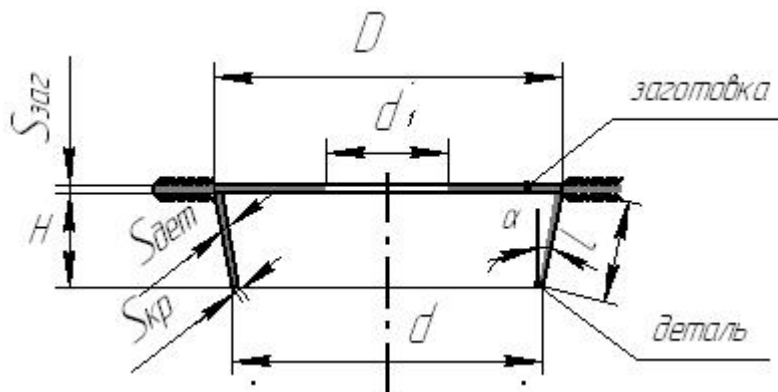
Схема процесса отбортовки из кольцевой заготовки:
